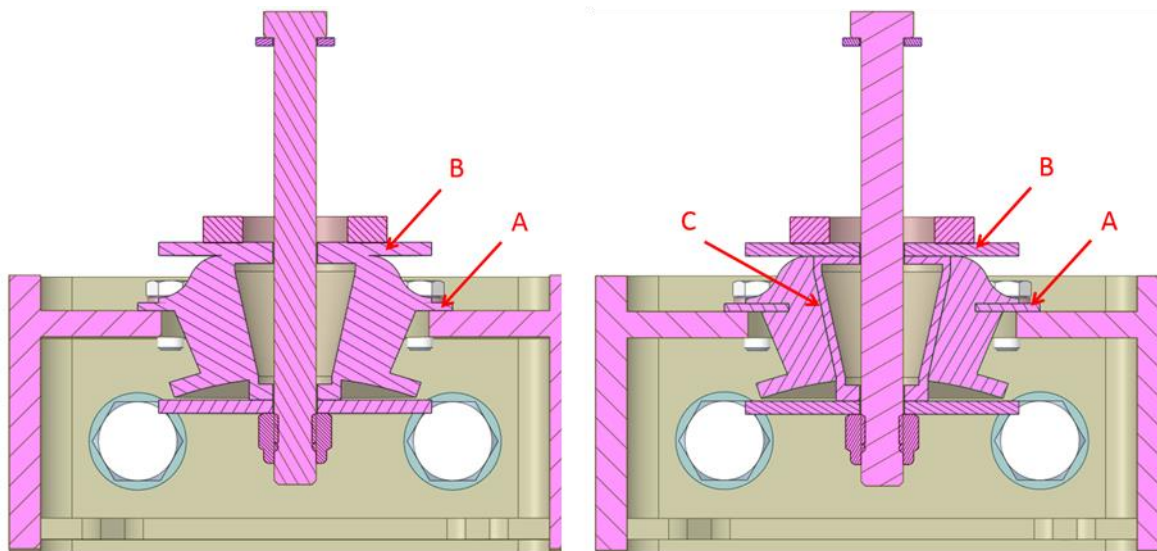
Sjednocení geometrie skeletu kabiny.
